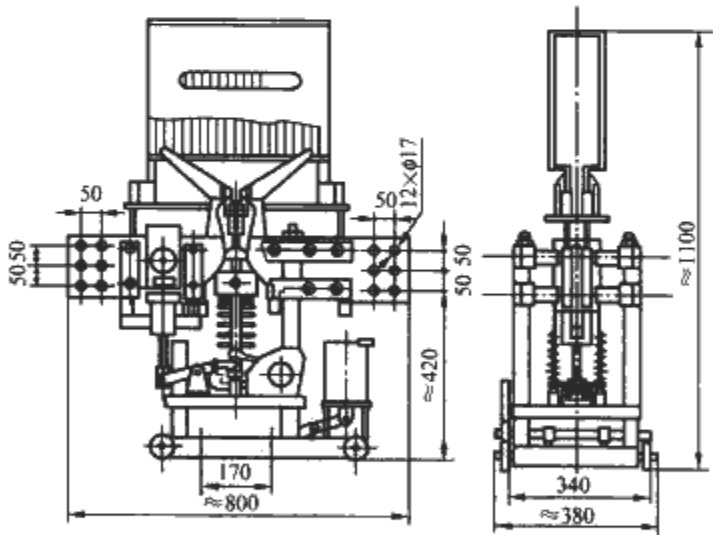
DS12-60/08 直流快速断路器的外形尺寸
